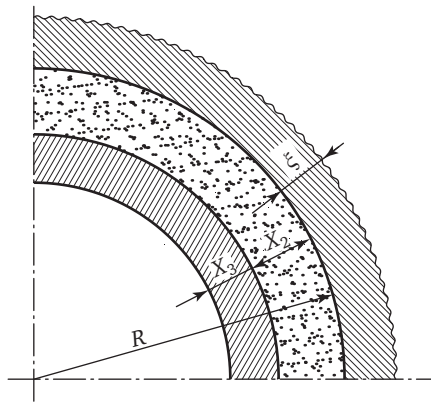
Схема затвердевания отливки со стороны металлооболочкового цилиндрического или шарового стержня
